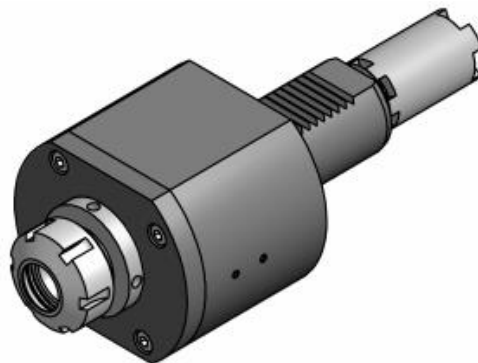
Осьова, свердлильно-фрезерна головка
